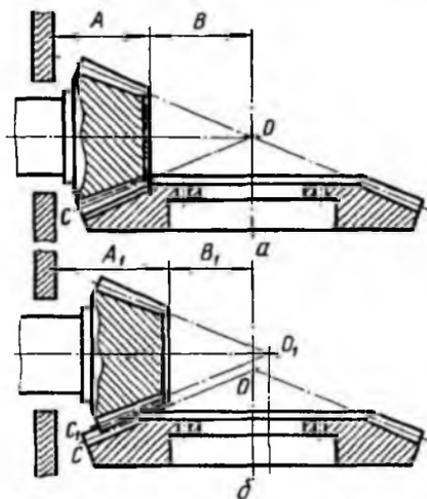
Схема регулировки зацепления зубчатых колес главной передачи:
